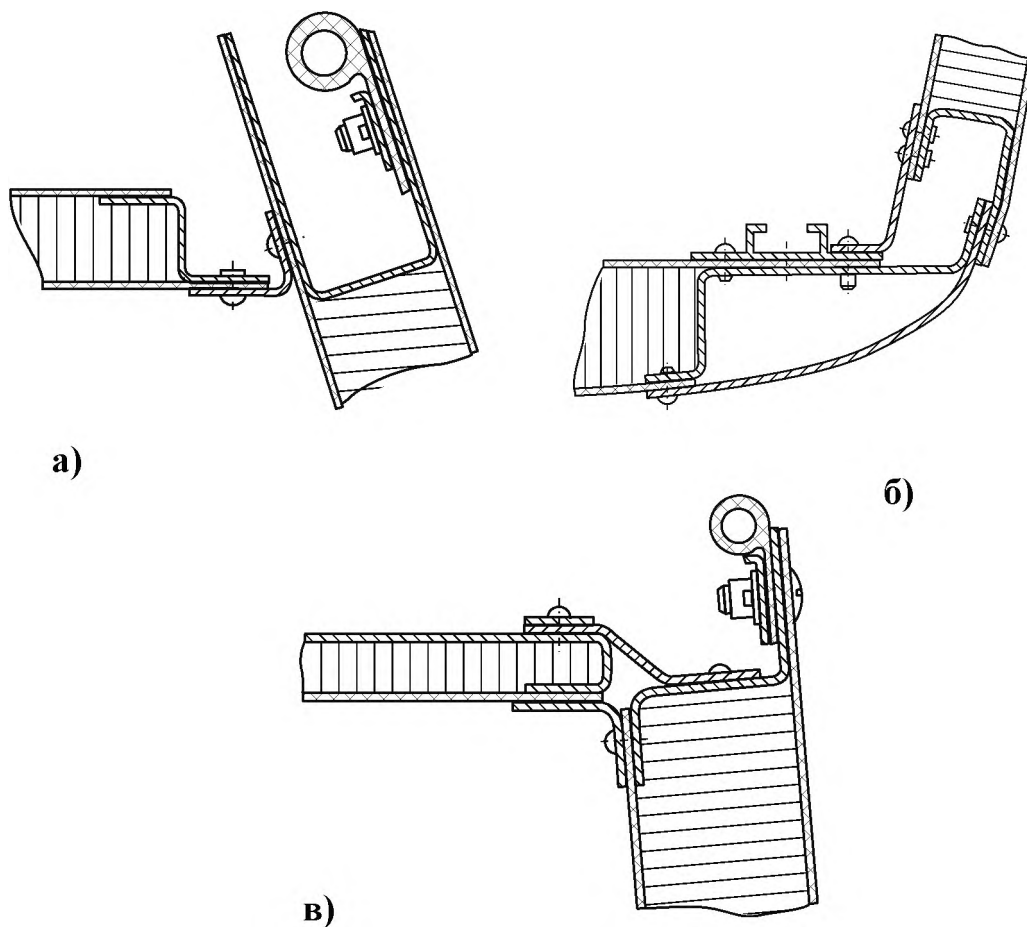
Крепление сотовых панелей в единую конструкцию кабины Ка-226А [12]:
